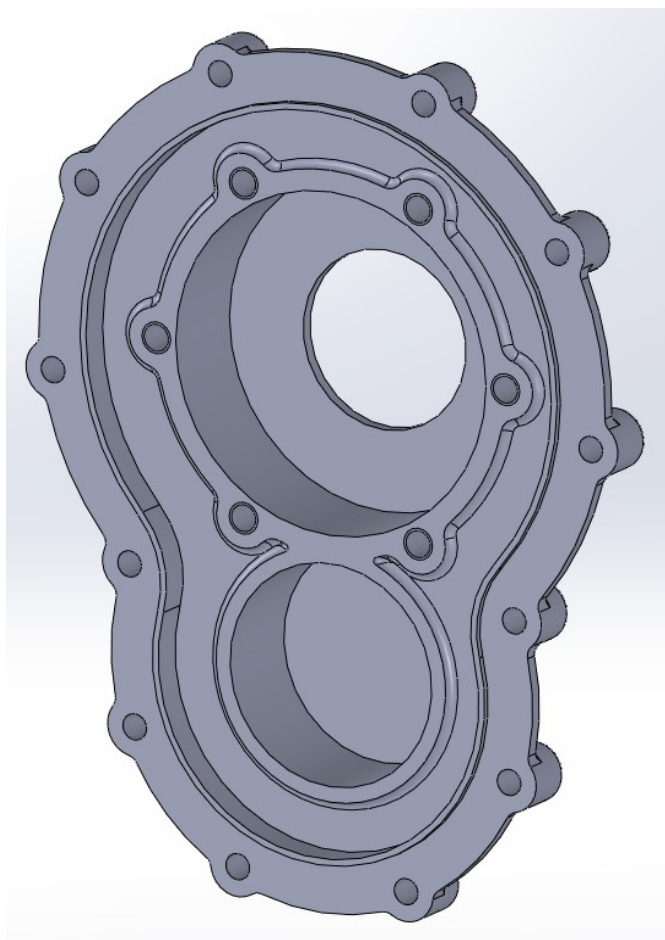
Carter lato elica, vista $\frac{3}{4}$ frontale –
